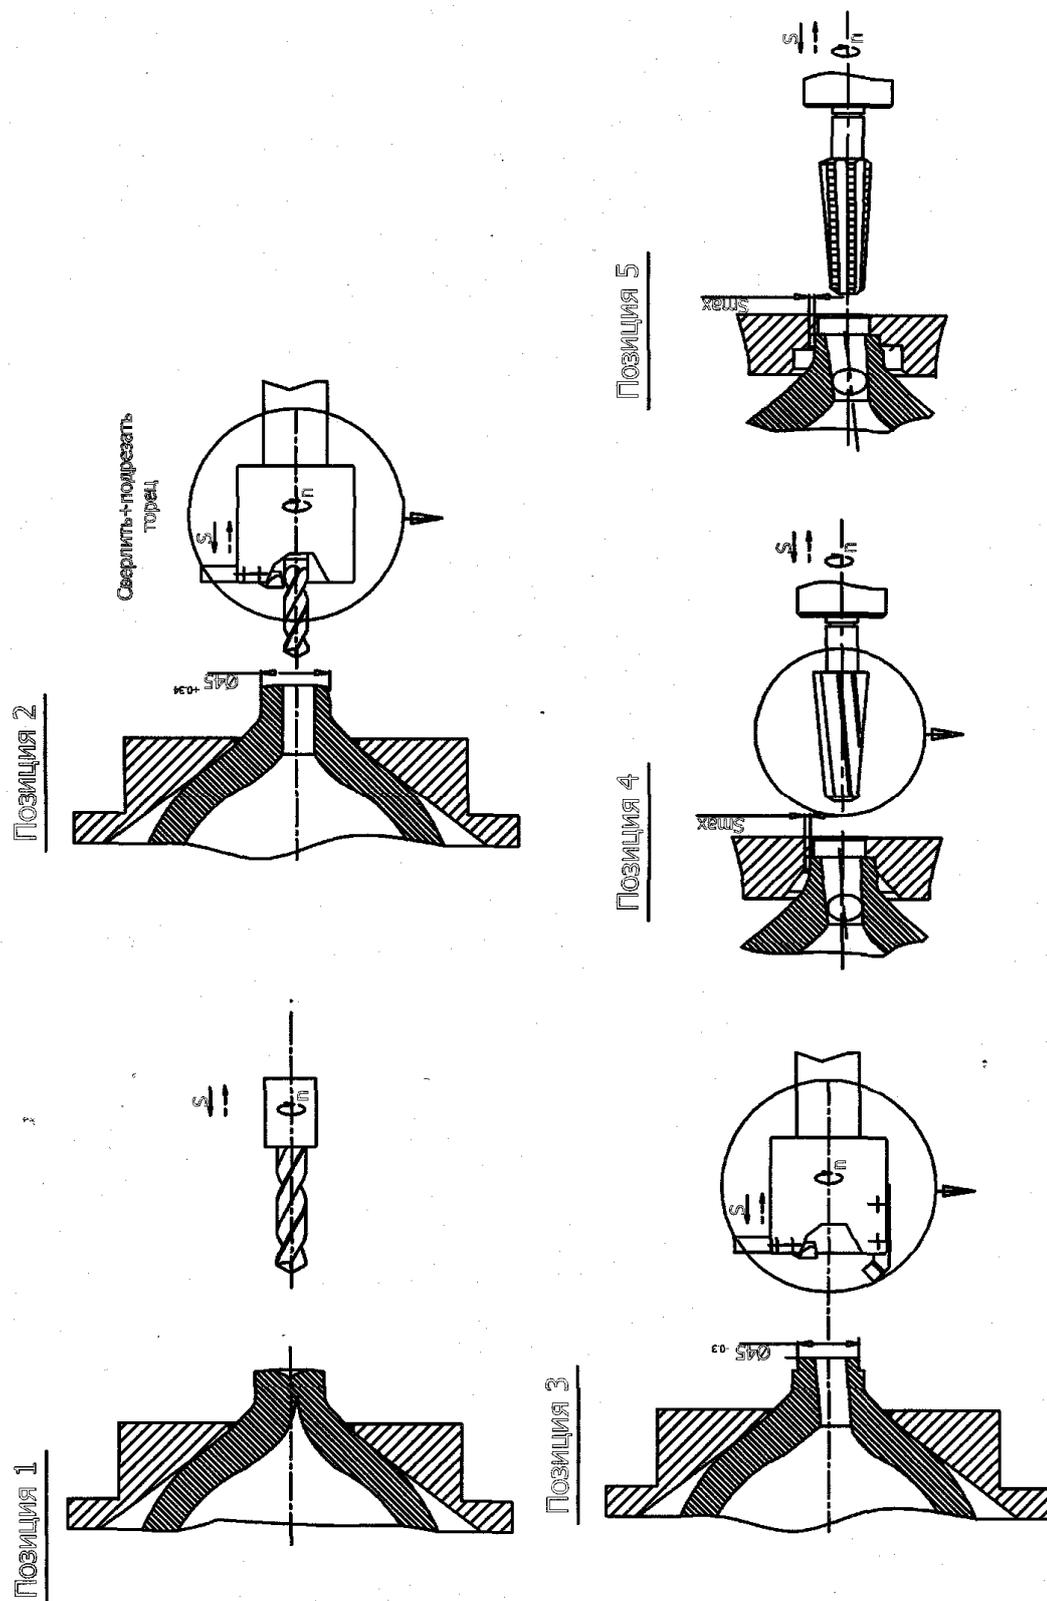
Действующий (базовый) технологический процесс механической обработки резьбового отверстия в горловине автомобильного баллона.
